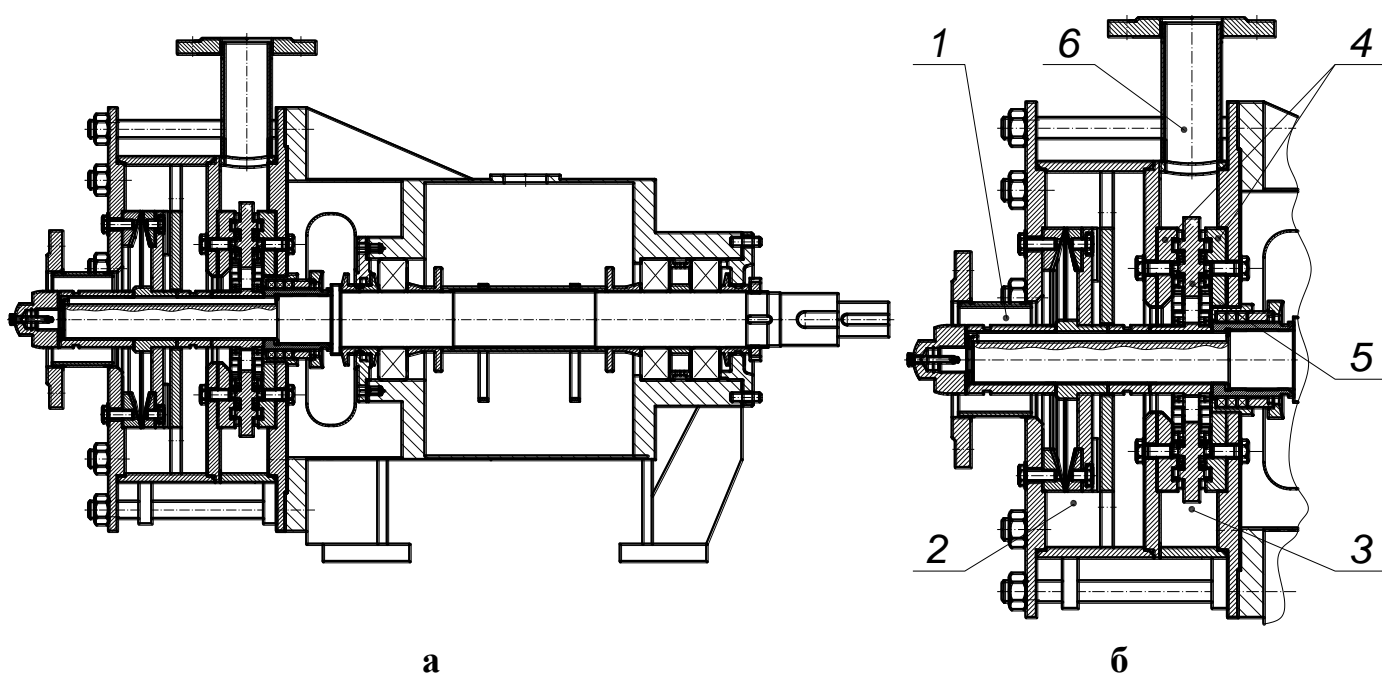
а – загальний вид ТГА; б – проточна частина машини
